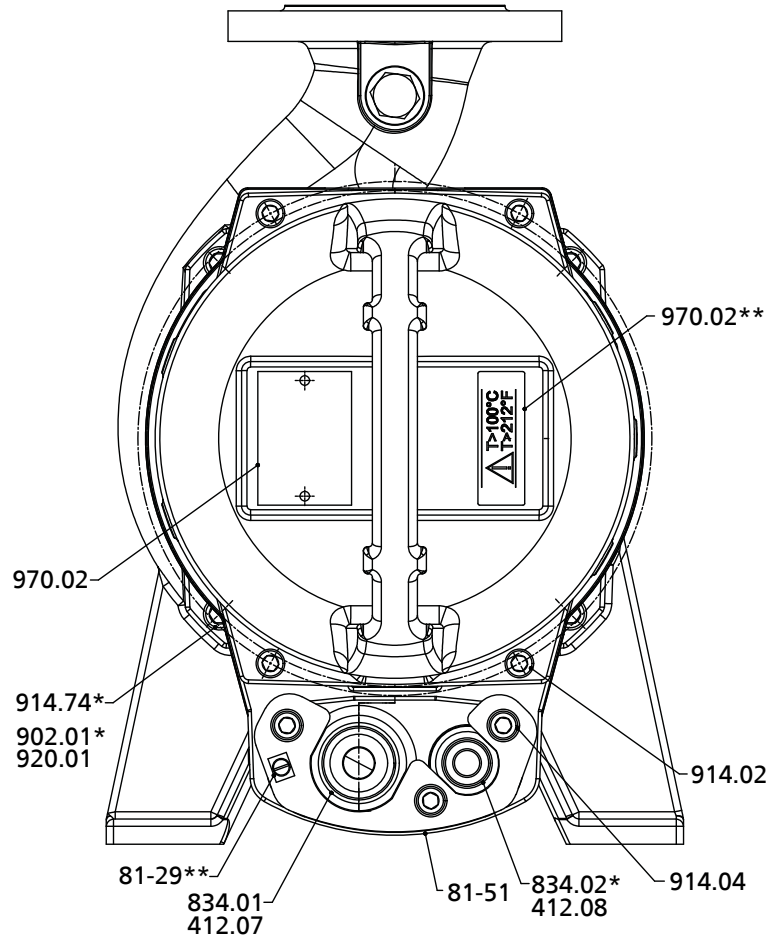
Motor und Befestigung Leitungsdurchführungen Amarex KRT
